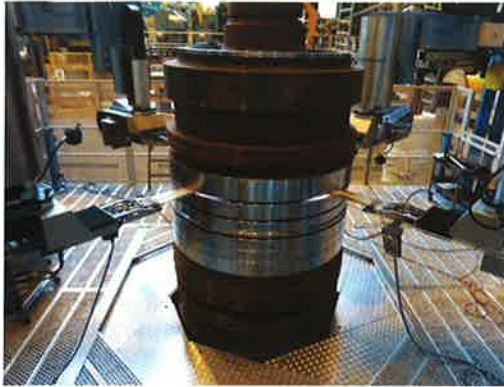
Schweißungen mit zwei oder vier Brennern (untere Lage mit einem Brenner und die darüberliegende Lage mit dem zweiten, um 180° versetzten Brenner. Bei dieser Methode können mehrerer Überschweißungen direkt hintereinander ohne Unterbrechung erfolgen. Dabei verwerfen sich die zu fügenden Werkstückteile nicht (Ausgleich der beim Schweißen entstehenden Zugspannungen).
